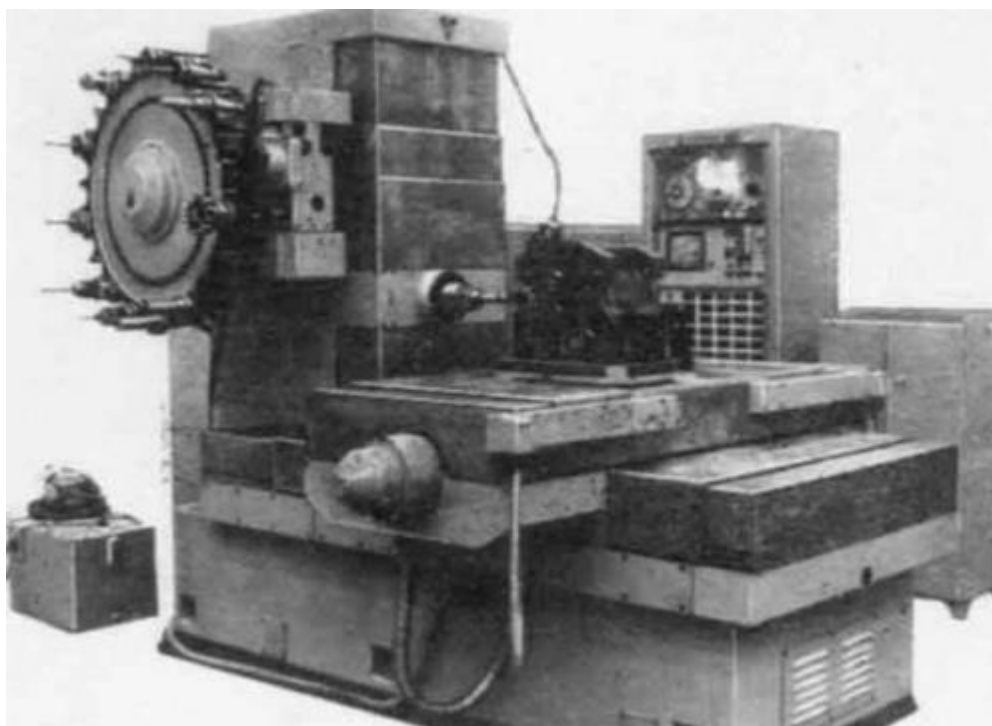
Горизонтальный обрабатывающий центр с барабаном
